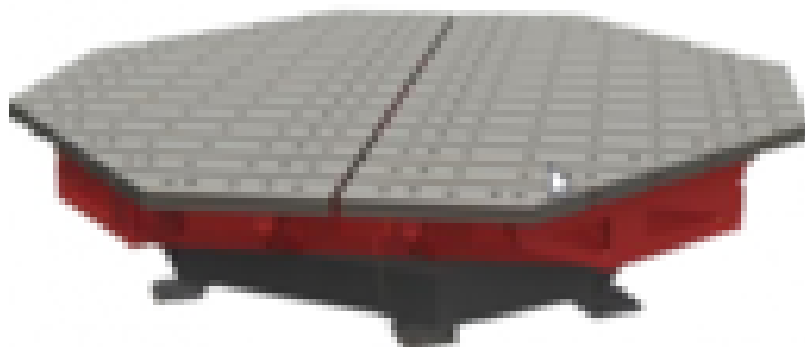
Вращающийся сварочный стол
